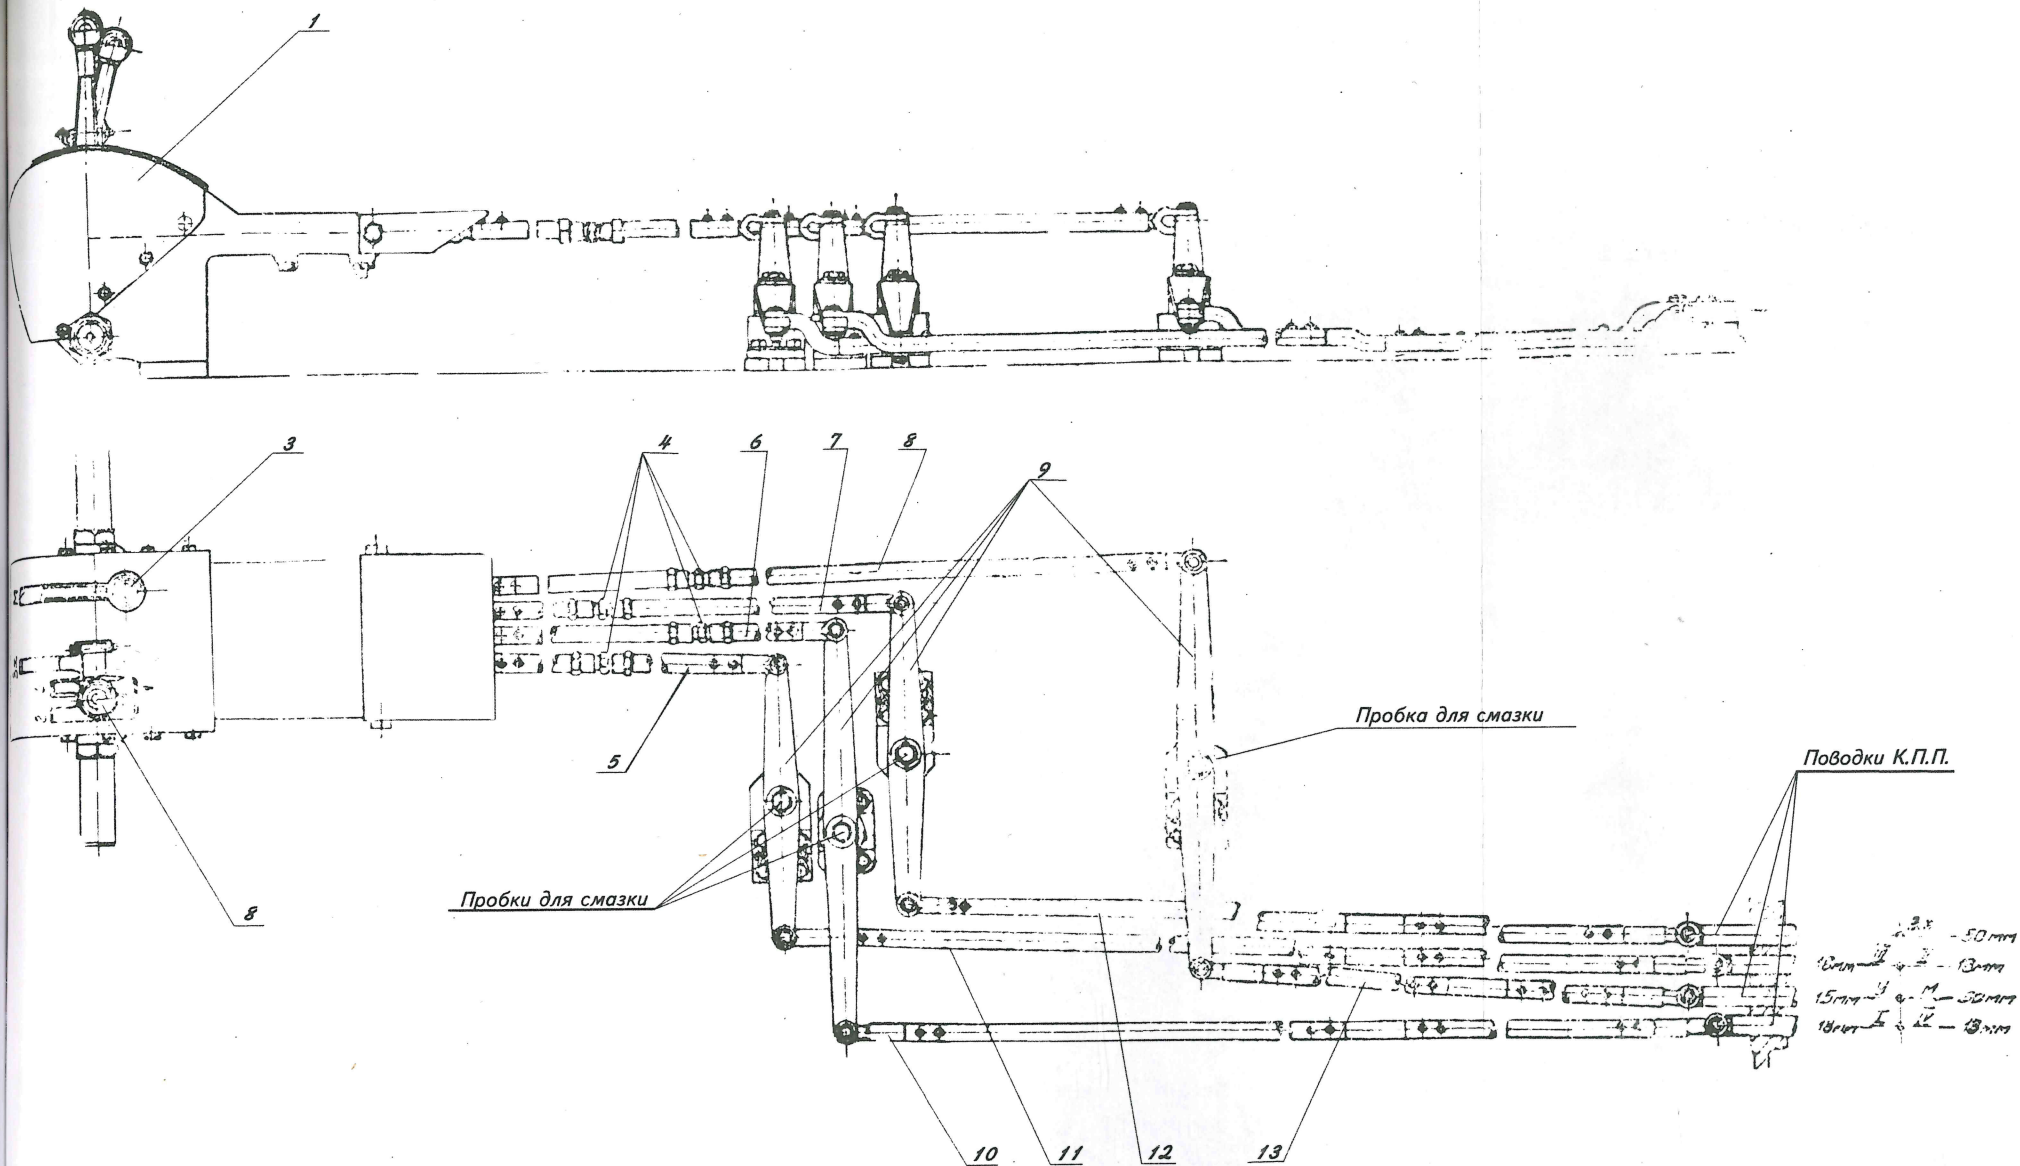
ПРИВОД УПРАВЛЕНИЯ КОРОБКЕЙ ПЕРЕМЕНЫ ПЕРЕДАЧ
